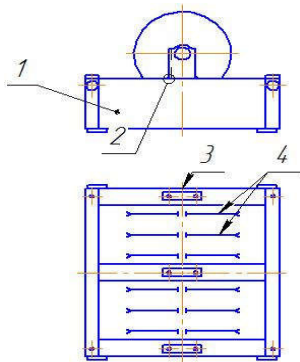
Принципова схема кронблоку: 1 – рама; 2 – зварний шов; 3 – вісь; 4 – блоки
